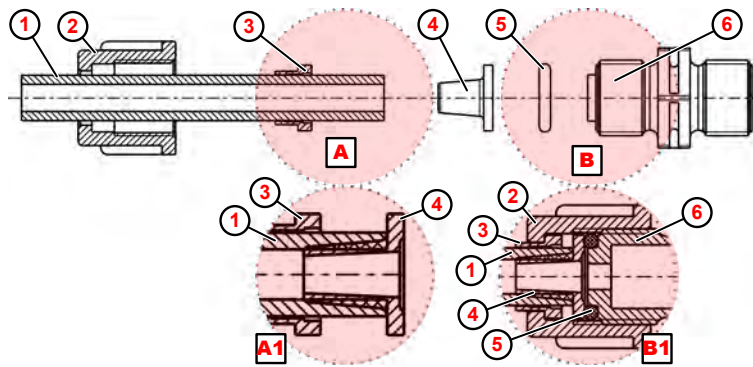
Rohr- Schlauchanschluss mit Kegelteil
